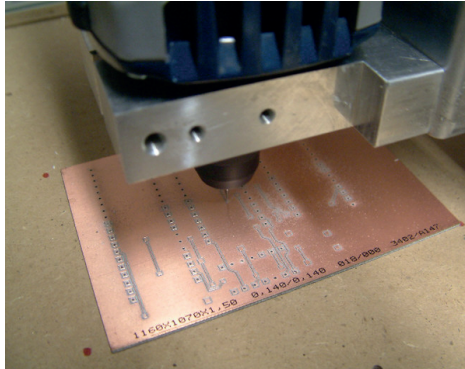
Фрезерование печатной платы на станке с ЧПУ
